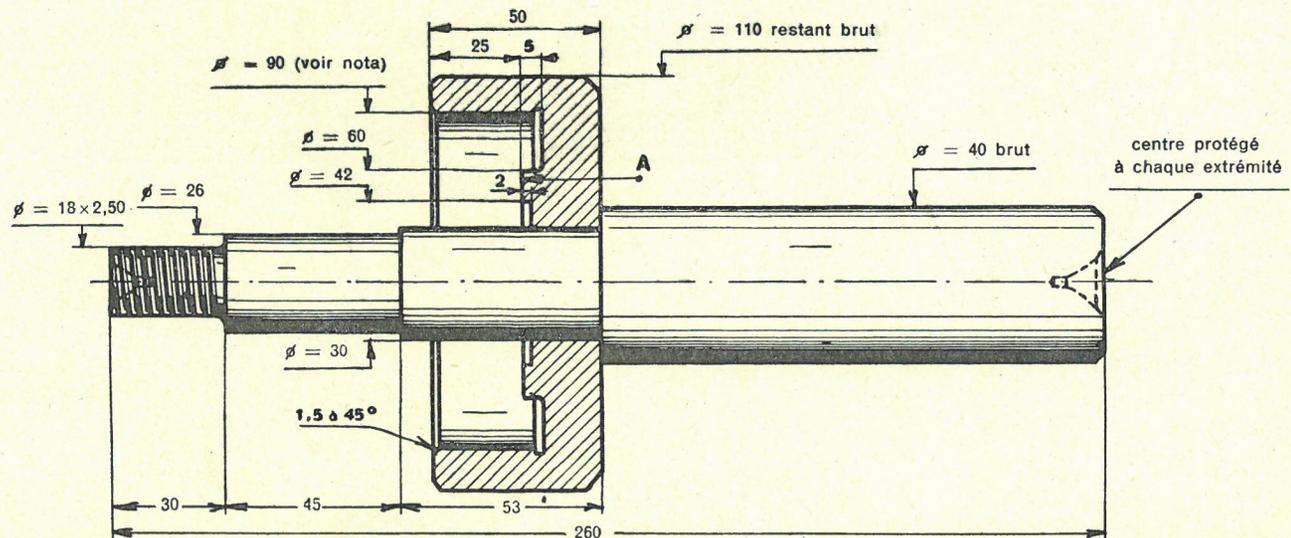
EMBOUT POUR RÉGLAGE DES CAMES
